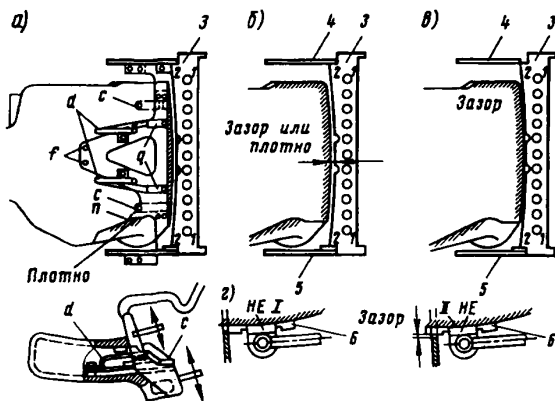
Проверка ударных поверхностей зева и малого зуба авто-сцепки профильной планкой 914р/24-1м шаблона 914р-м
